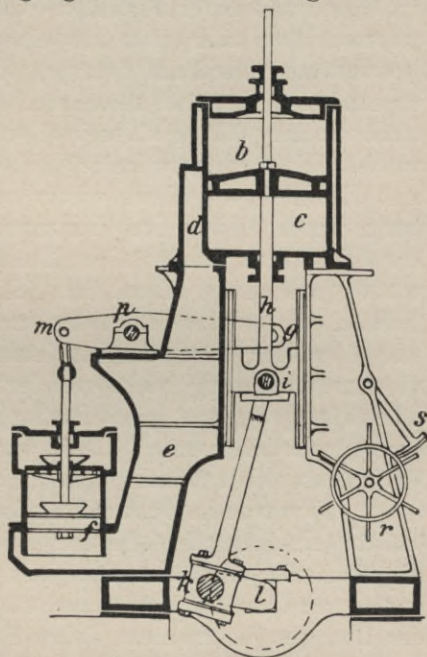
Hammermaschine des Lloyd-Dampfers „Falke“.
